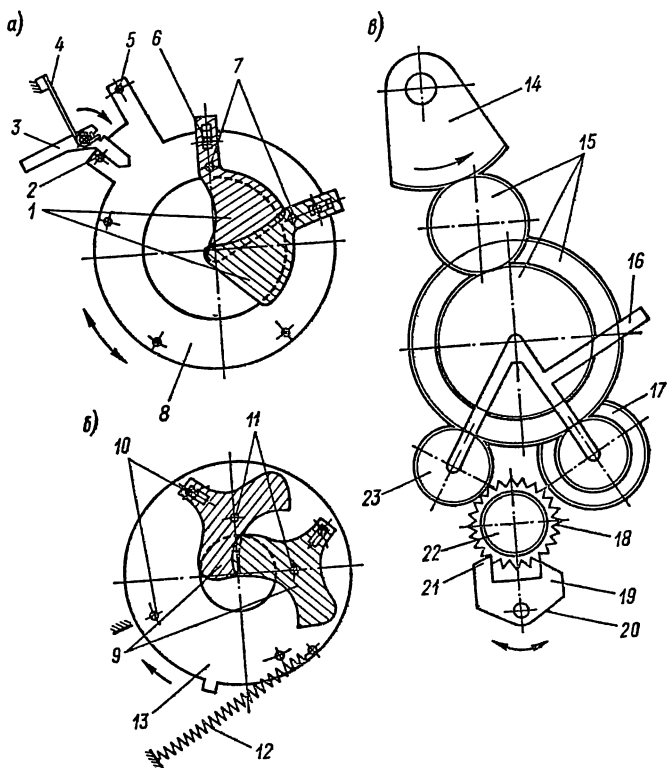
Приводы лепестков и анкерного регулятора центральных фотозатворов; а — с возвратно-поворотным движением лепестков; б — с двусторонними лепестками; в — анкерный регулятор выдержек
